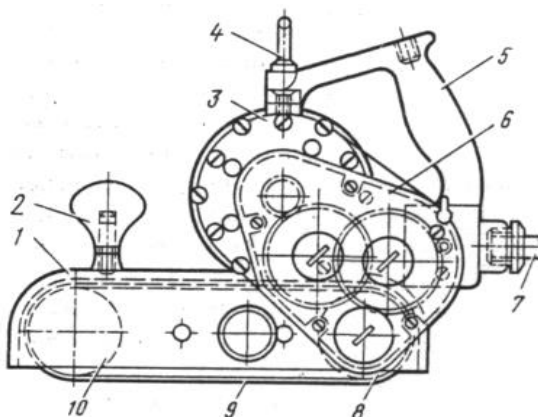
Электрическая шлифовальная машинка с бесконечной лентой: 1 - кожух; 2 - рукоятка опорная; 3 - электродвигатель; 4 - кольцо для подвески машинки; 5 - рукоятка с курковым выключателем; 6 - редуктор; 7 - провод; 8 - барабан ведущий; 9 - лента шлифовальная; 10 - барабан натяжной
